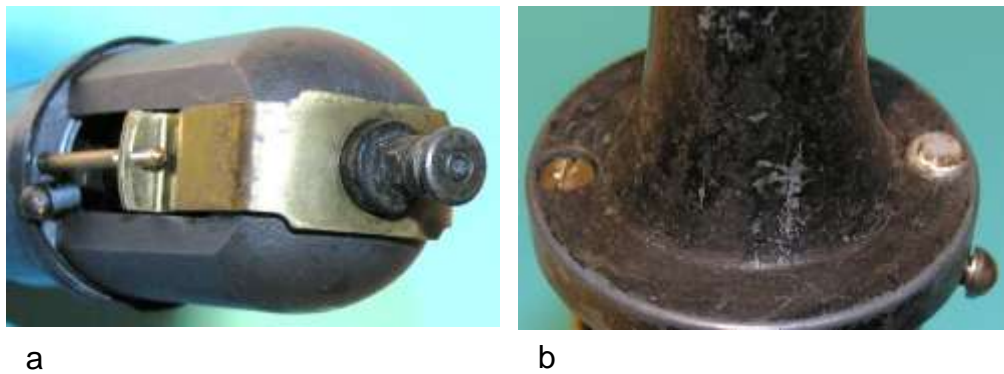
Befestigung des Magneten mit dem Spannblech: a) Position des Spannblechs in der Pollücke, b) Schraubenköpfe im Lagerhalsfuß
